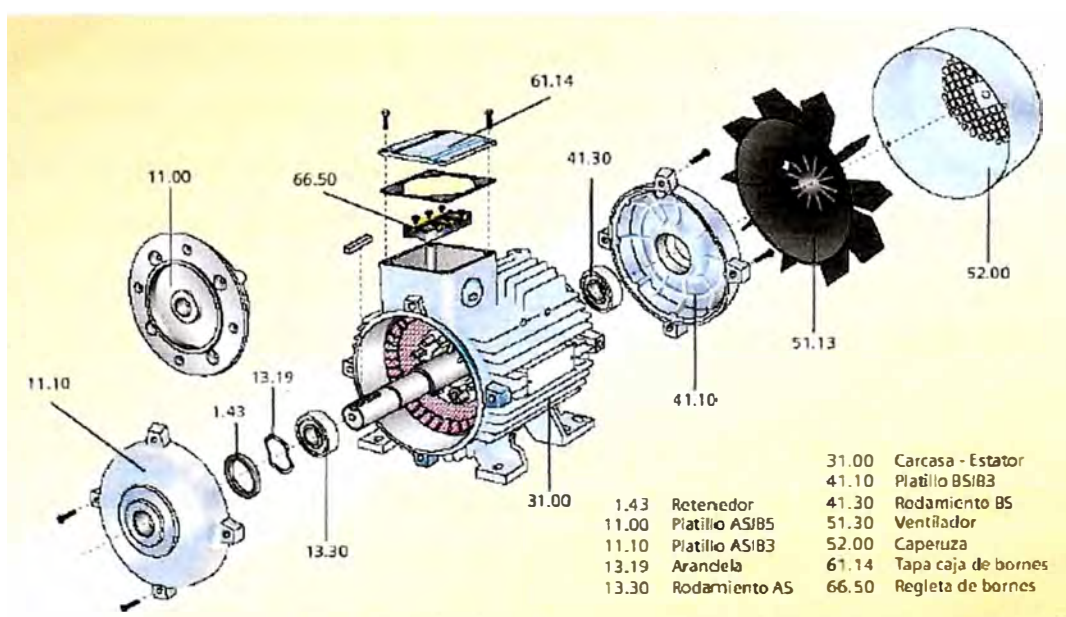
Despiece de un motor de inducción industrial de rotor de jaula de ardilla [9]
